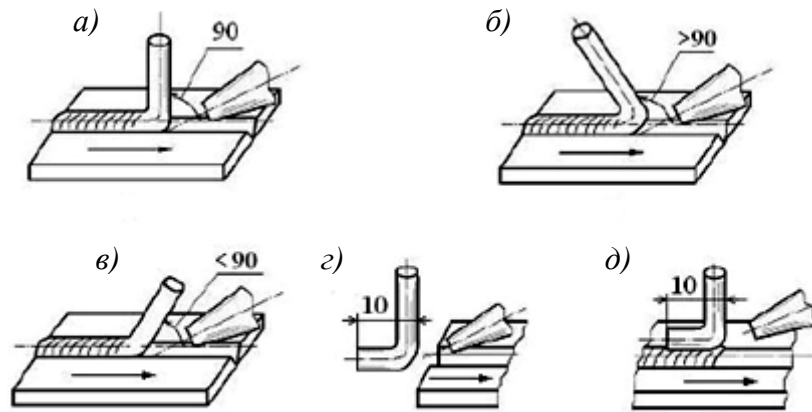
Положение присадочного прутка и горелки при сварке
